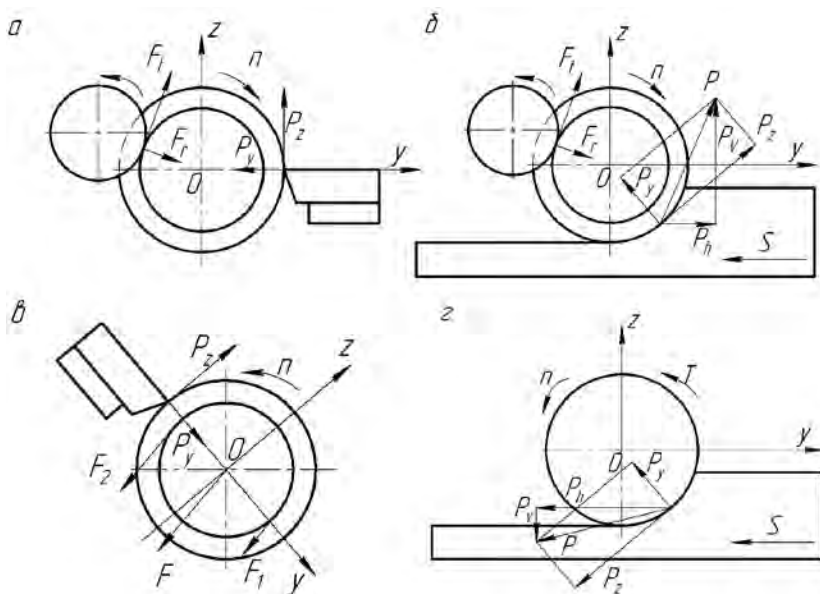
Расчетные схемы нагрузок на шпиндель от сил резания и приводного элемента в виде зубчатого колеса (*а, б*), шкива ременной передачи (*в*) и зубчатой муфты, шлицевого соединения или шкива на разгрузочном устройстве (*г*)
